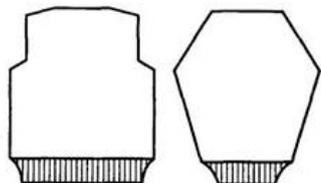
Детали для изготовления трикотажных изделий регулярным способом
